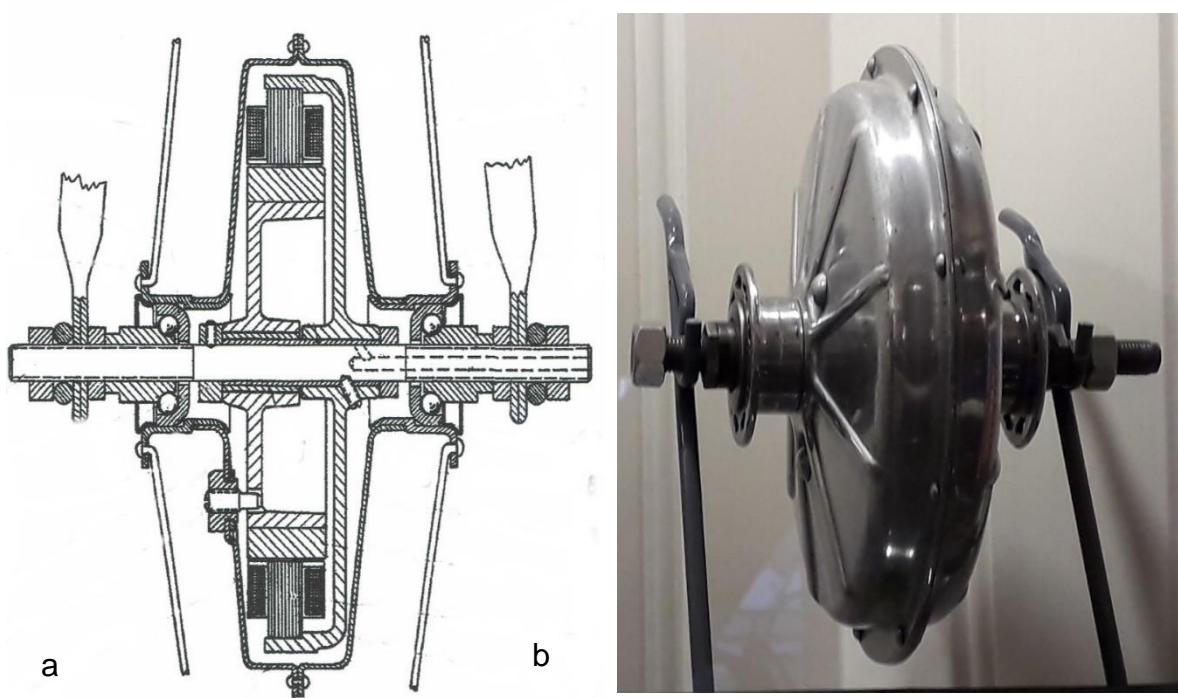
Innenpolrad mit einem Anker mit ausgeprägten Polen: a) Zeichnung im Patent / 21/, b) Exemplar im Velorama Fahrradmuseum in Nijmegen, Niederlande, Besitzer, Geerd-Jan Moed
